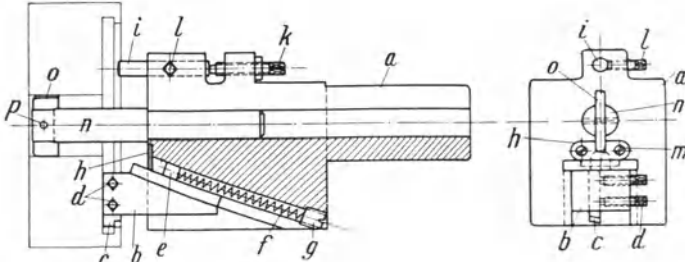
Hinterstechvorrichtung mit Ausbohrwerkzeug.
